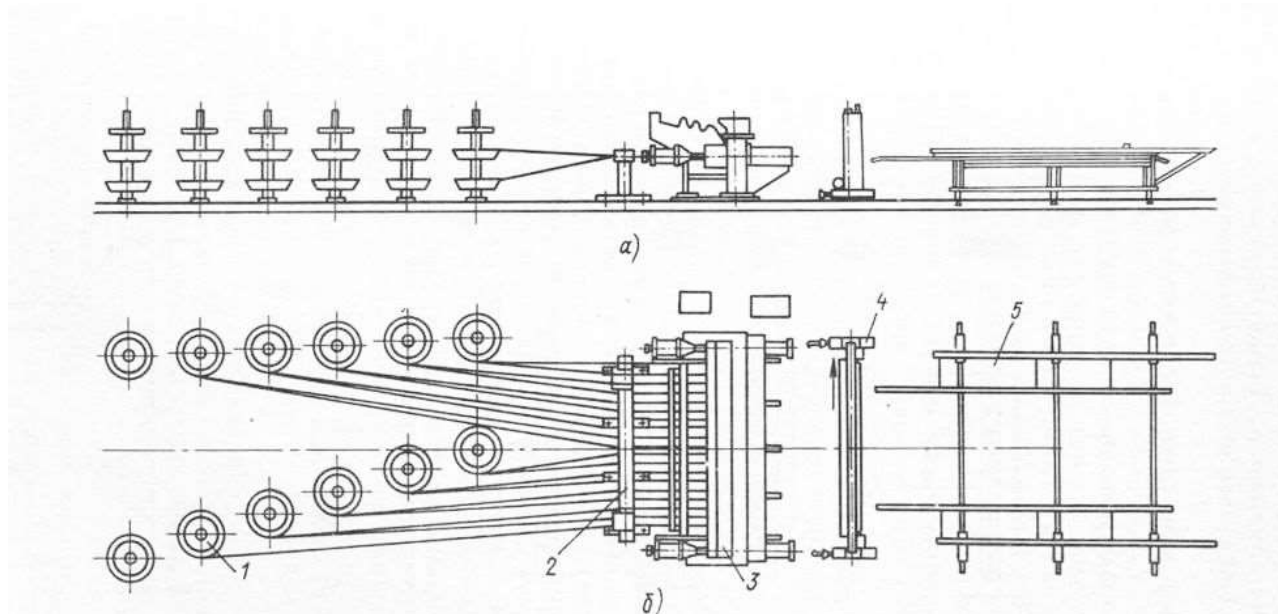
Автоматизированная линия 7975/1 для изготовления арматурных сеток шириной до 3,8 м: а – вид сбоку, б – вид сверху; 1 – двухъярусная вертушка СМЖ-495А, 2 – правильное устройство СМЖ-775, 3 – машина для сварки сеток МТМ-160, 4 – ножницы СМЖ-771; 5 – пакетировщик сеток СМЖ-61Г
